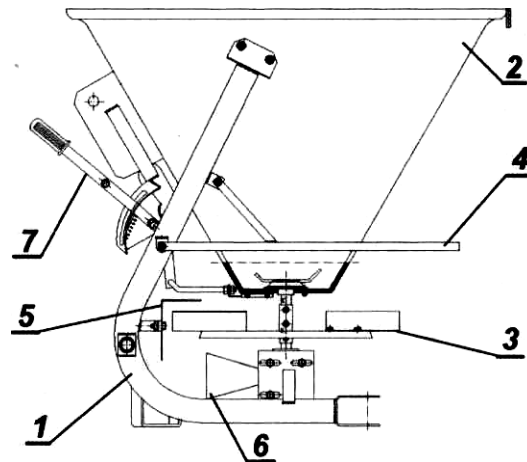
Загальний вигляд розкидача: 1 – рама; 2 – бак; 3 – розсіваючий апарат; 4 – захист; 5 – щиток; 6 – кожух; 7 – дозуючий пристрій.
